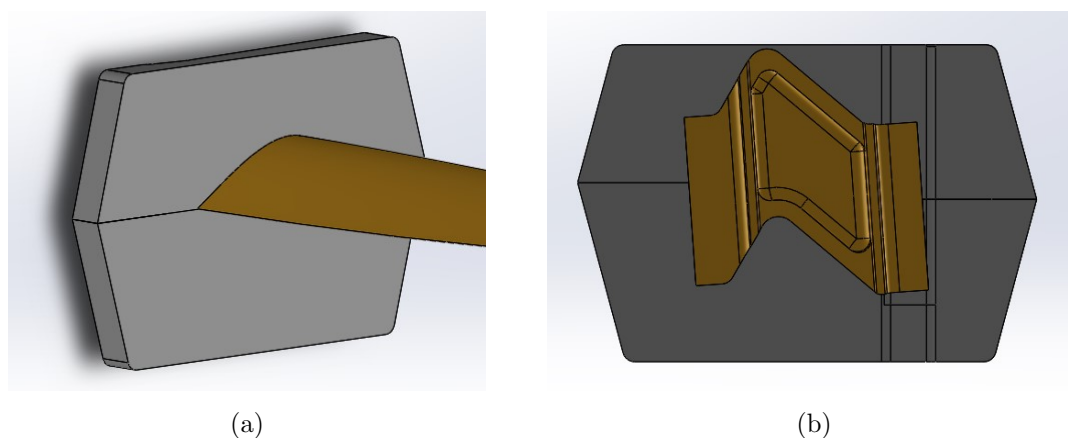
Solução construtiva adotada para remoção da peça do molde, a) vista traseira, b) vista frontal
